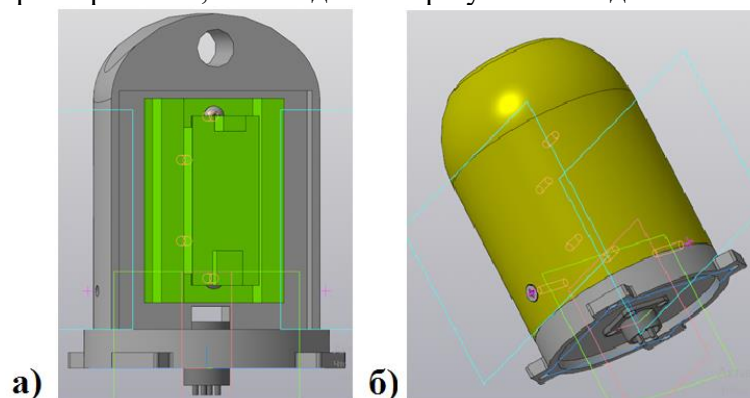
3Д модель ГРК: а) Размещение контроллера Arduino Nano на корпусе б) Конечный вид конструкции корпуса вместе с защитным кожухом
